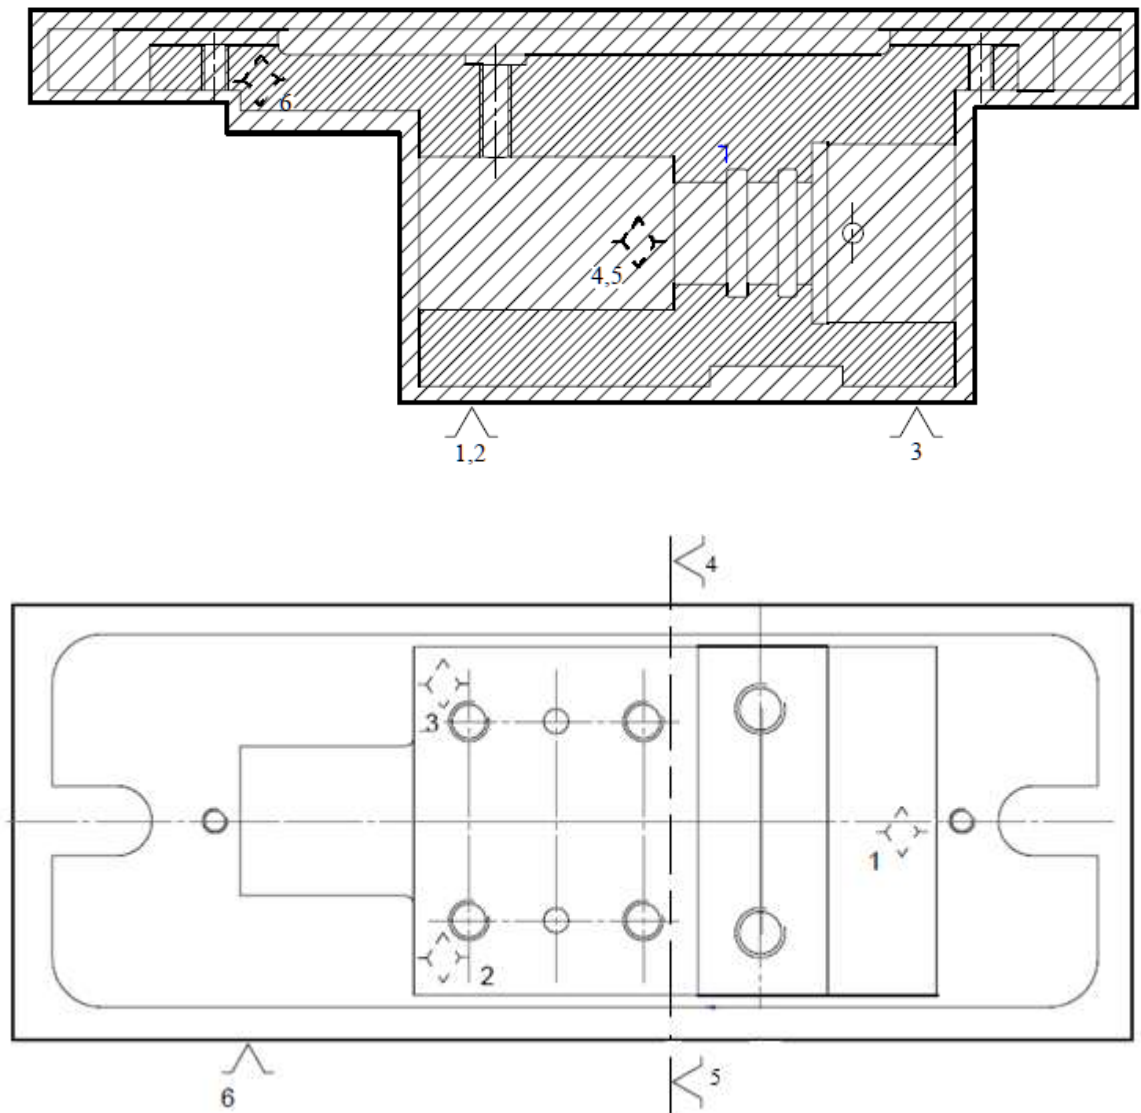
Теоретична схема базування по технологічним базам деталі «Корпус»
